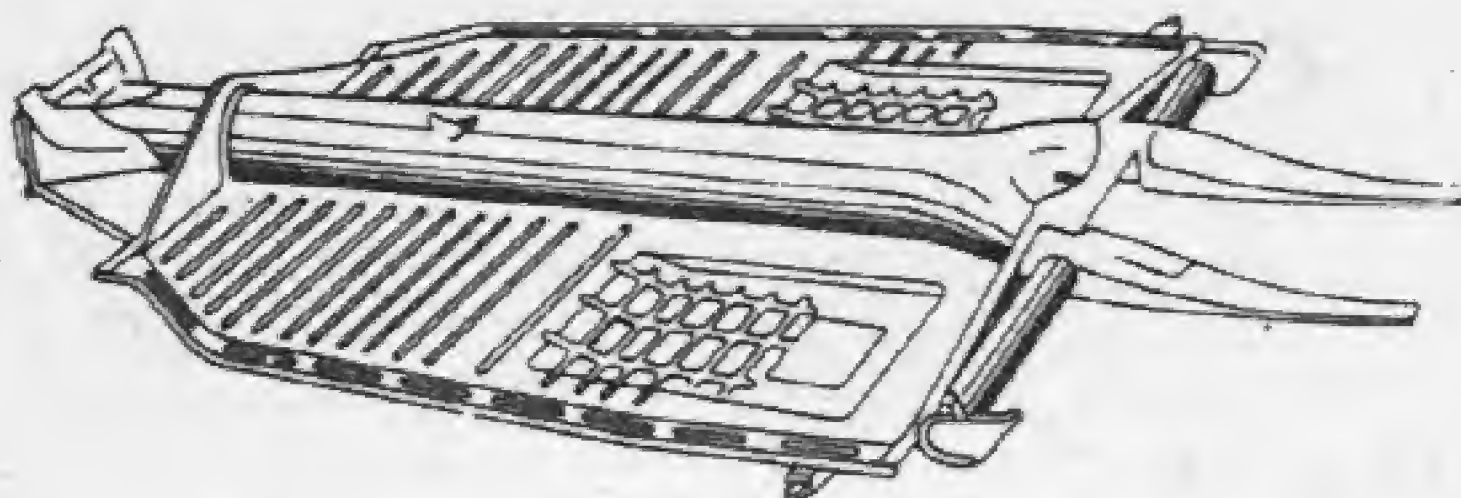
Chasis con viga central y plataforma soldada con dos largueros en un extremo para servir de apoyo al motor.
